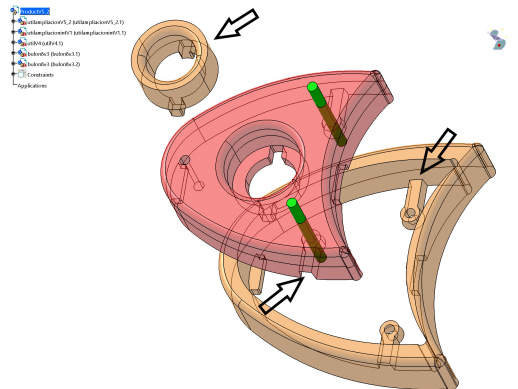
Versión 2 utillaje modular: Conjunto ensamblado con útil de ampliación.
